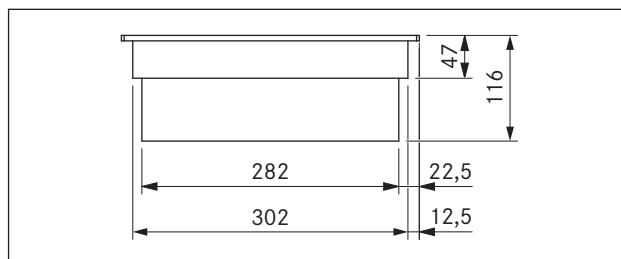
CKIW dimensioni apparecchio vista frontale
